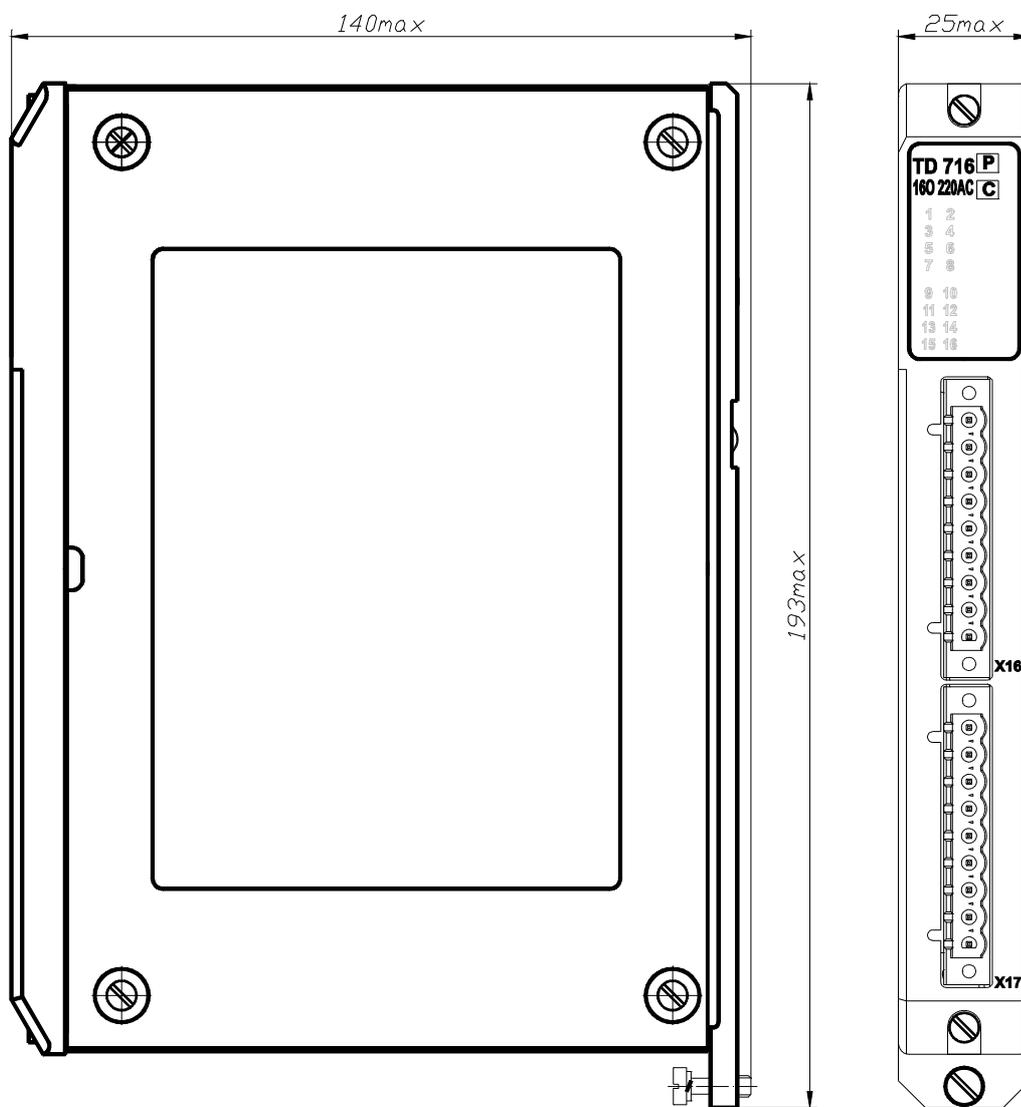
Внешний вид и габаритные размеры модуля TD 716
